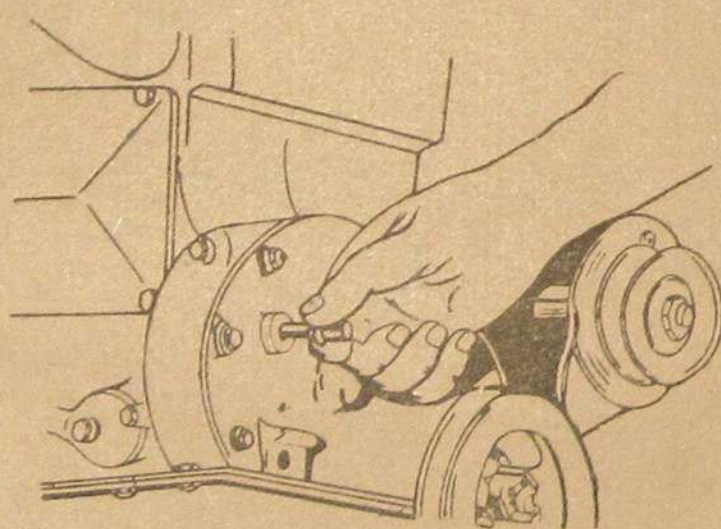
Установка поршня в ВМТ двигателя ГАЗ-42
